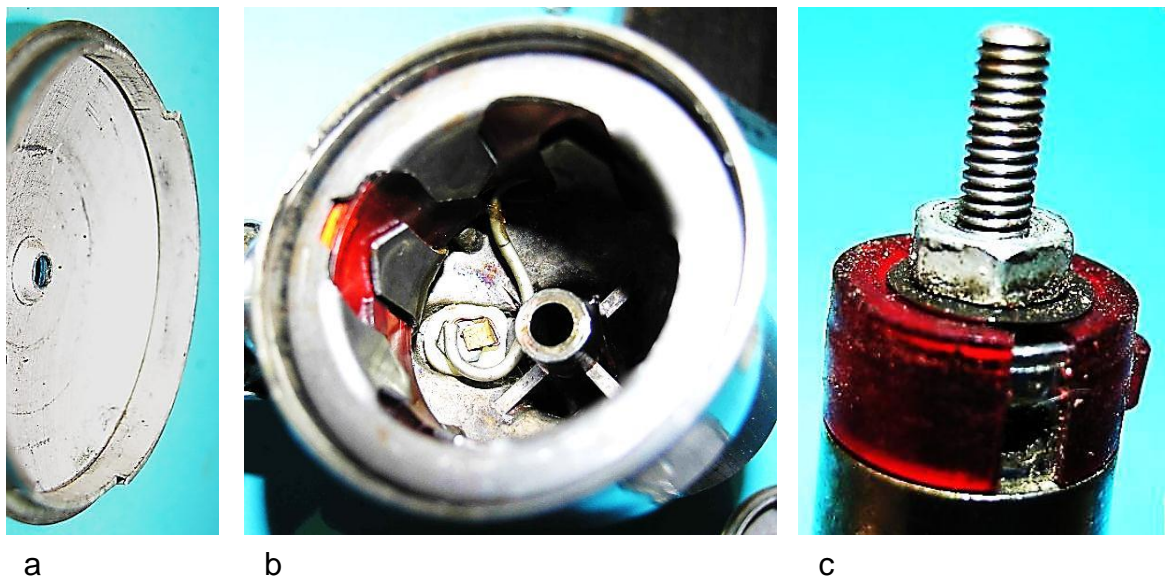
Baugruppen: a) Boden, b) Anker, c) Öllochabdeckung
